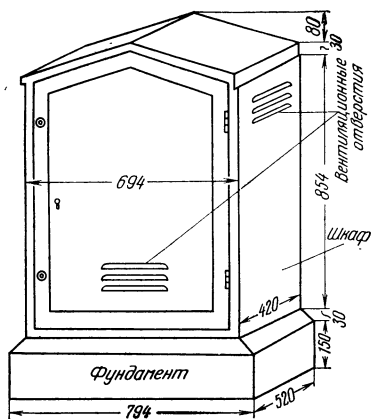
Шкаф на фундаменте для установки электродренажа
